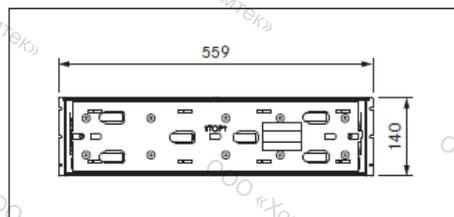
Размеры прибора, модель MS140, вид спереди
